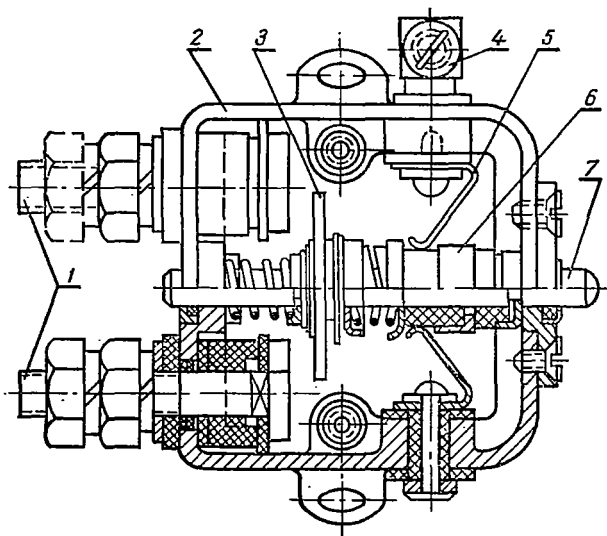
Включатель ВК14 стартера СТ8 (без крышки):
